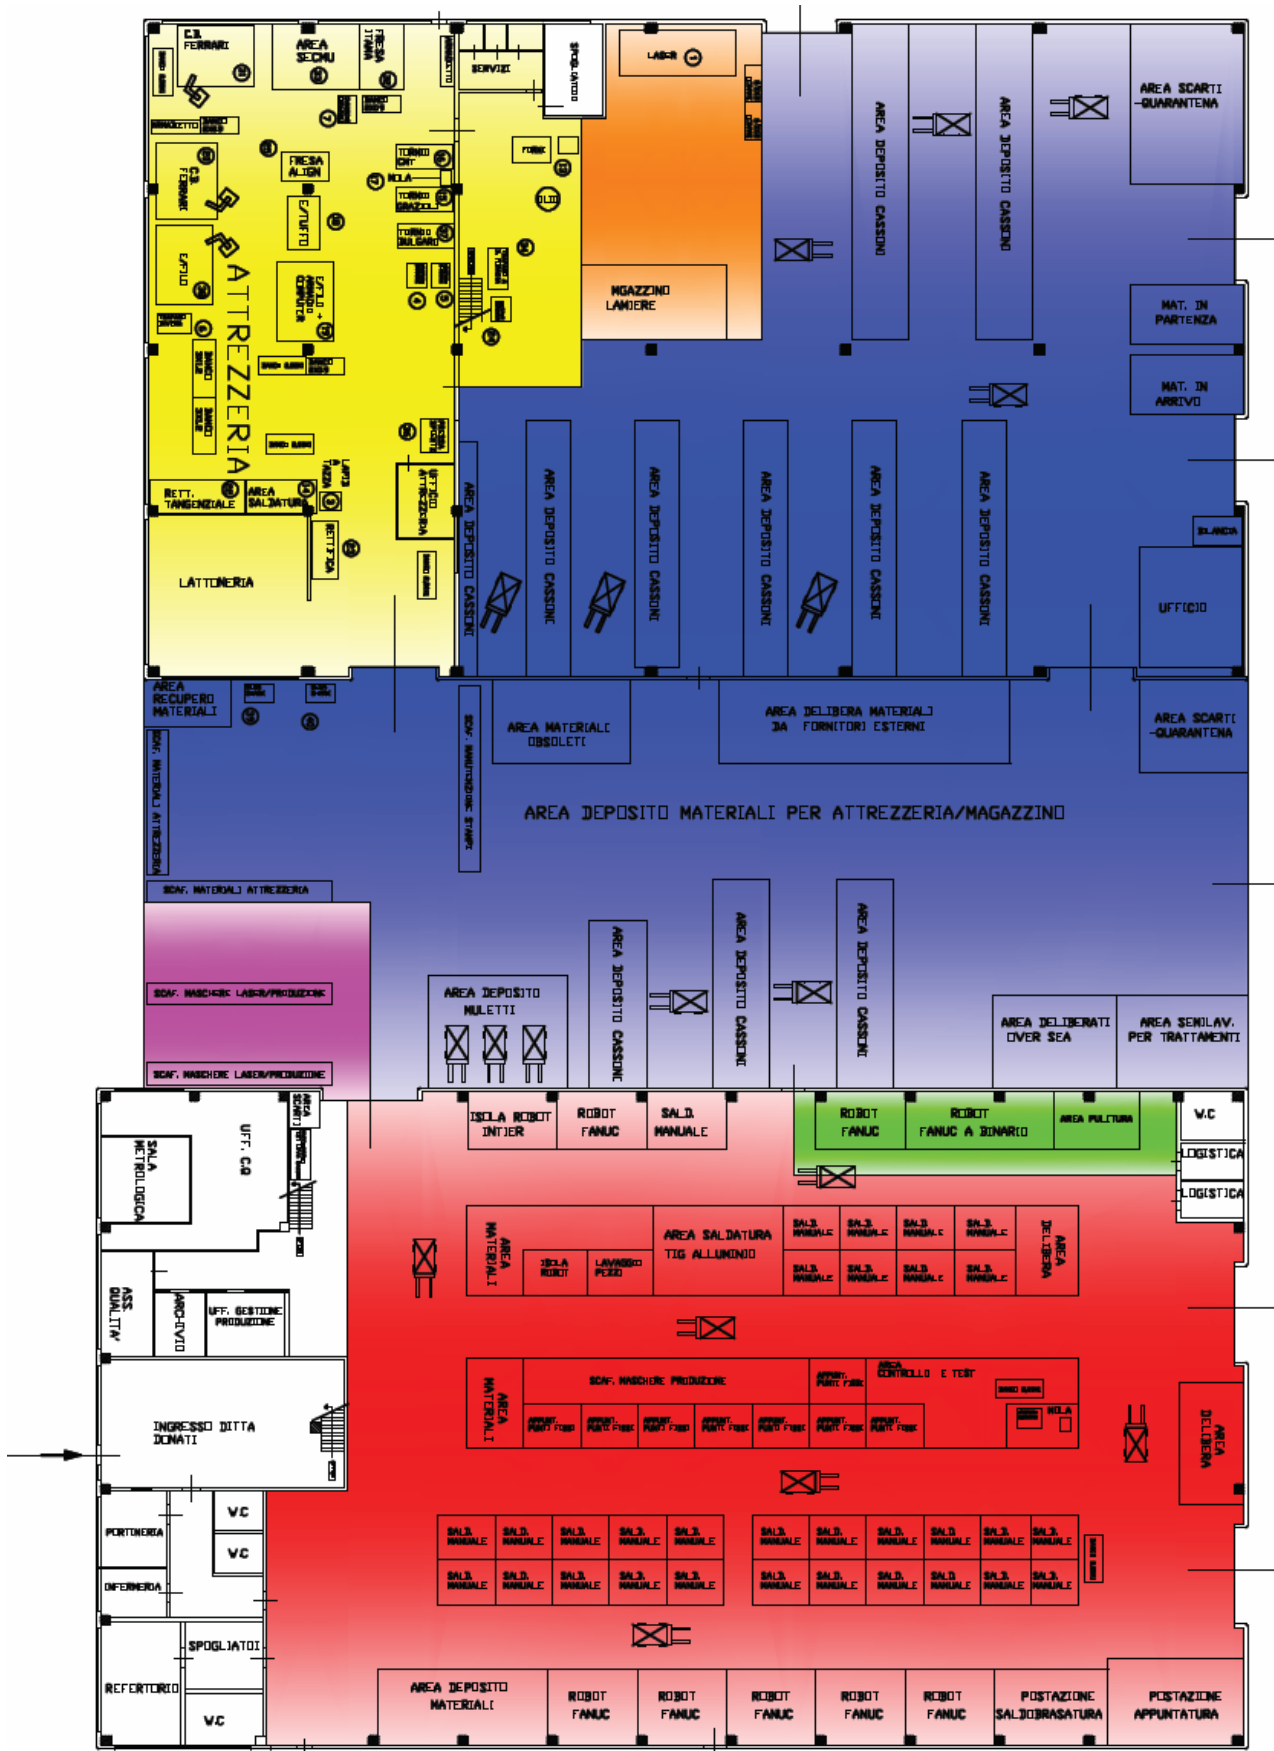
divisione planimetrica dei reparti all'interno dello stabilimento
